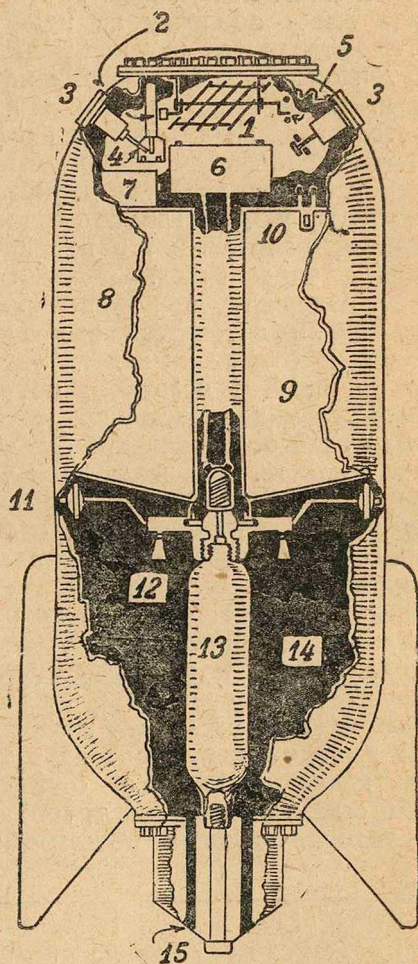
Глубоководная (подвижная) магнитная мина; 1—магнитный прибор; 2—тормоз; 3—гидростатические приборы; 4—ртутный контакт; 5—контакт для выпуска сжатого воздуха; 6—сухая батарея; 7—обмотка; 8—немагнитная оболочка; 9—взрывчатое вещество; 10—детонатор; 11—воздушный клапан; 12—воздушный выпуск; 13—баллон с сжатым воздухом; 14—водяной балласт; 15—отверстия для выхода воды и воздуха.
